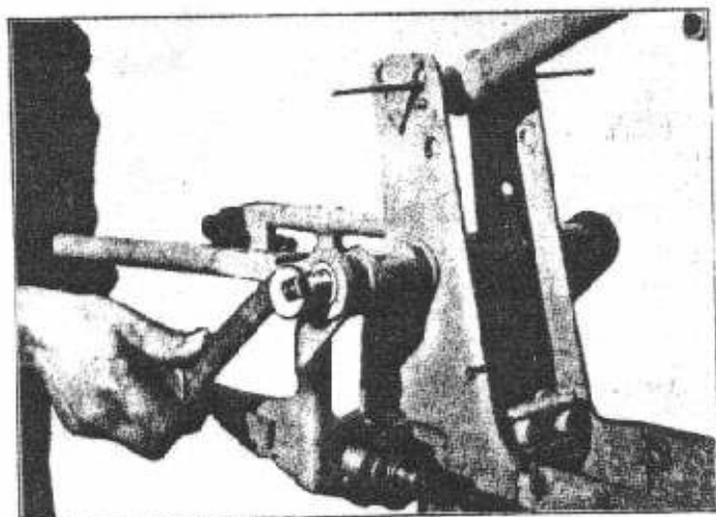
Come si leva il perno principale del forcellone oscillante.
